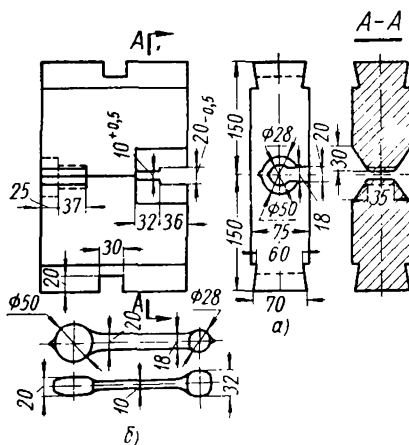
Фигурные бойки для ковки заготовки шатуна на молоте: *a* — бойки; *б* — заготовки шатуна
